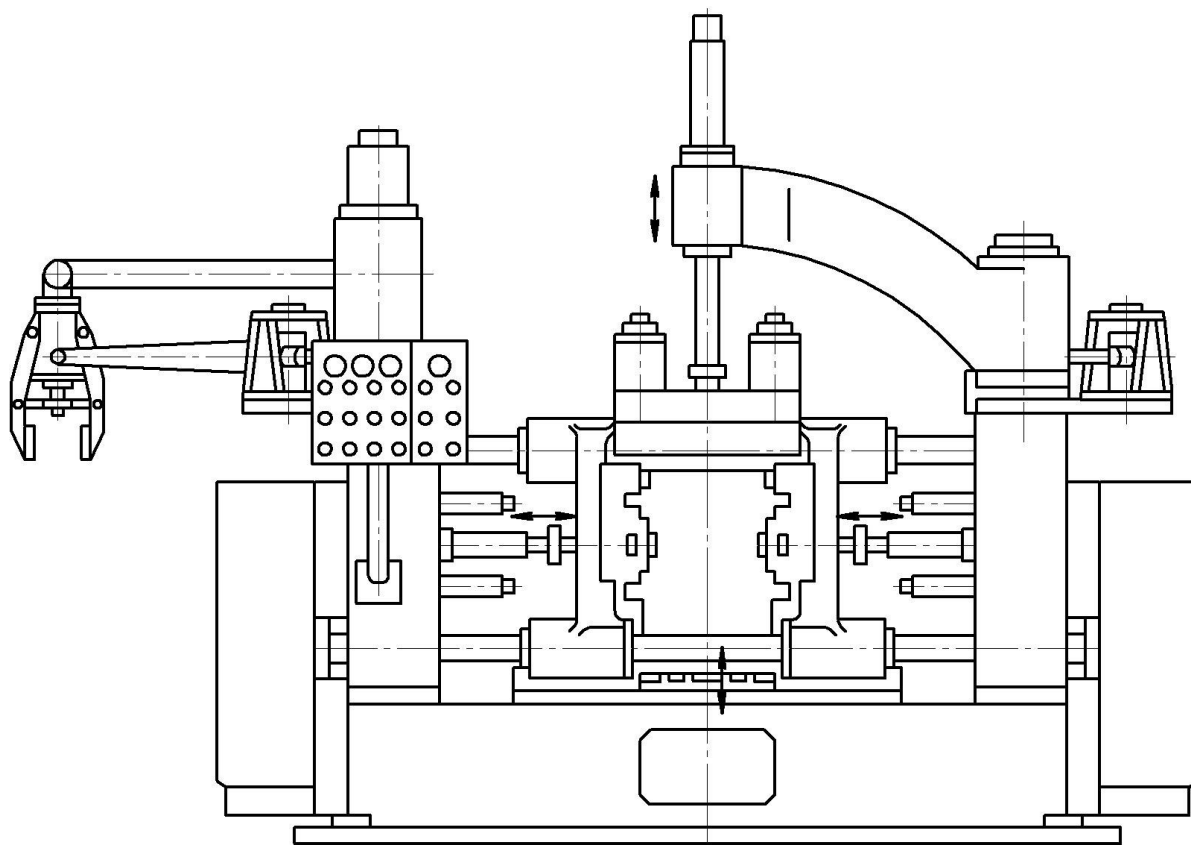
Загальний вид однопозиційної універсальної
